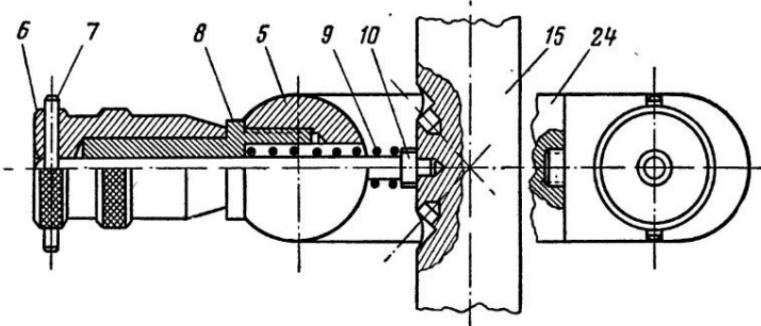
Модель механизма подачи суппорта токарного станка (узел фиксатора «трензеля»): 5 — кронштейн; 6 — гильза; 7 — конусная шпилька; 8 — втулка; 9 — пружина; 10 — фиксатор; 15 — стойка; 24 — планка.
